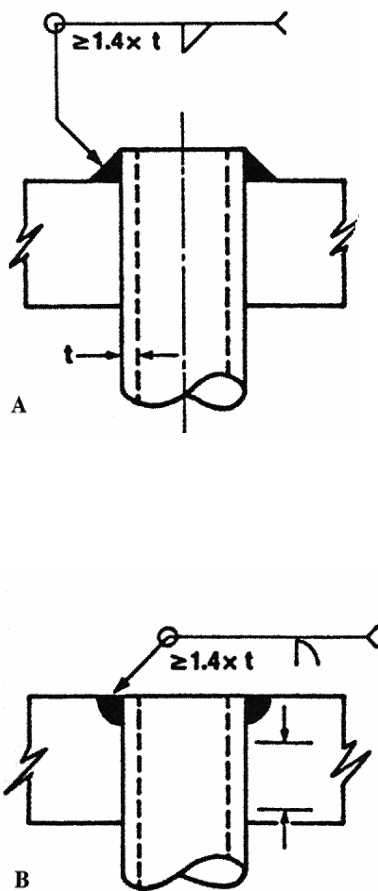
Типичное соединение трубка – трубная доска с высокой механической прочностью. А – сварка внахлест; В – сварка в разделку.
